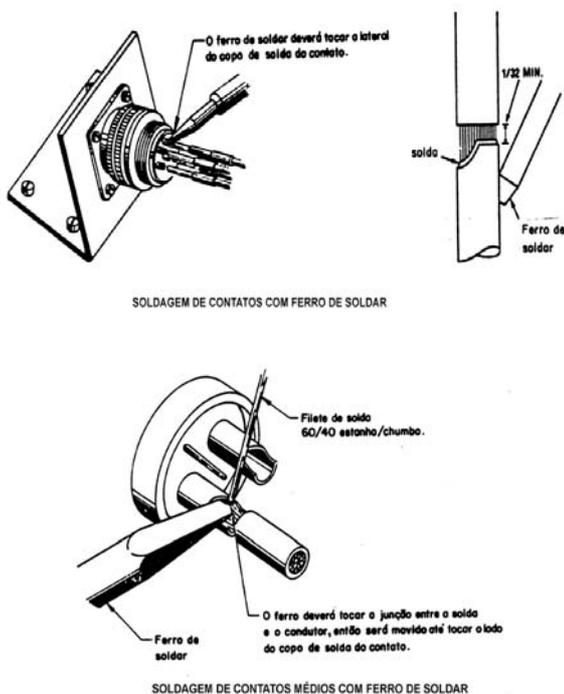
Soldagem de acordo com o tamanho dos contatos
